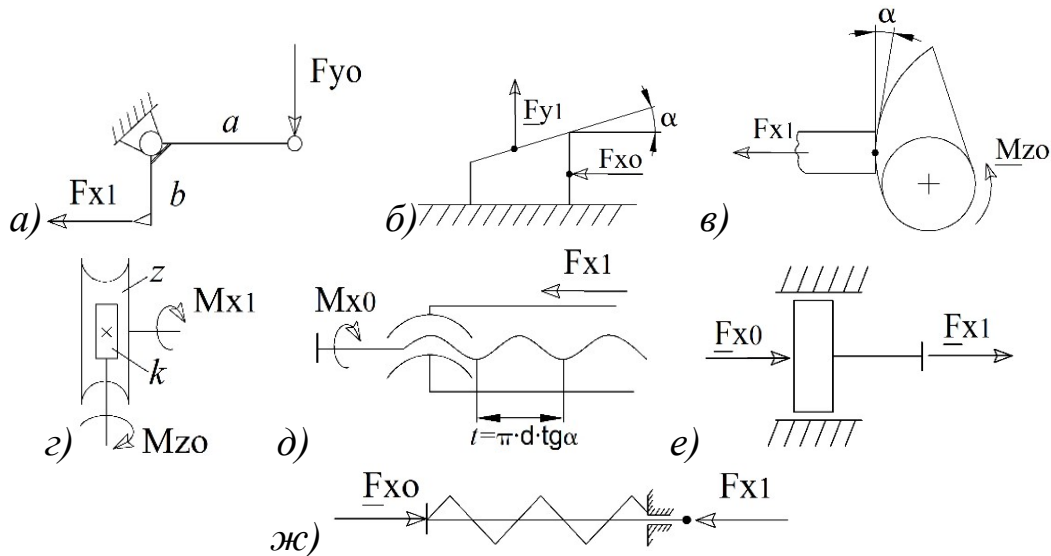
Варіанти механічних перетворювачів енергії ПрЗ токарного автомата: а – важіль (LV); б – клин (WD); в – спіраль (SP); г – зубчата передача (GR); д – гвинт (SC); е – плунжер (PL); ж – пружина (SR)
